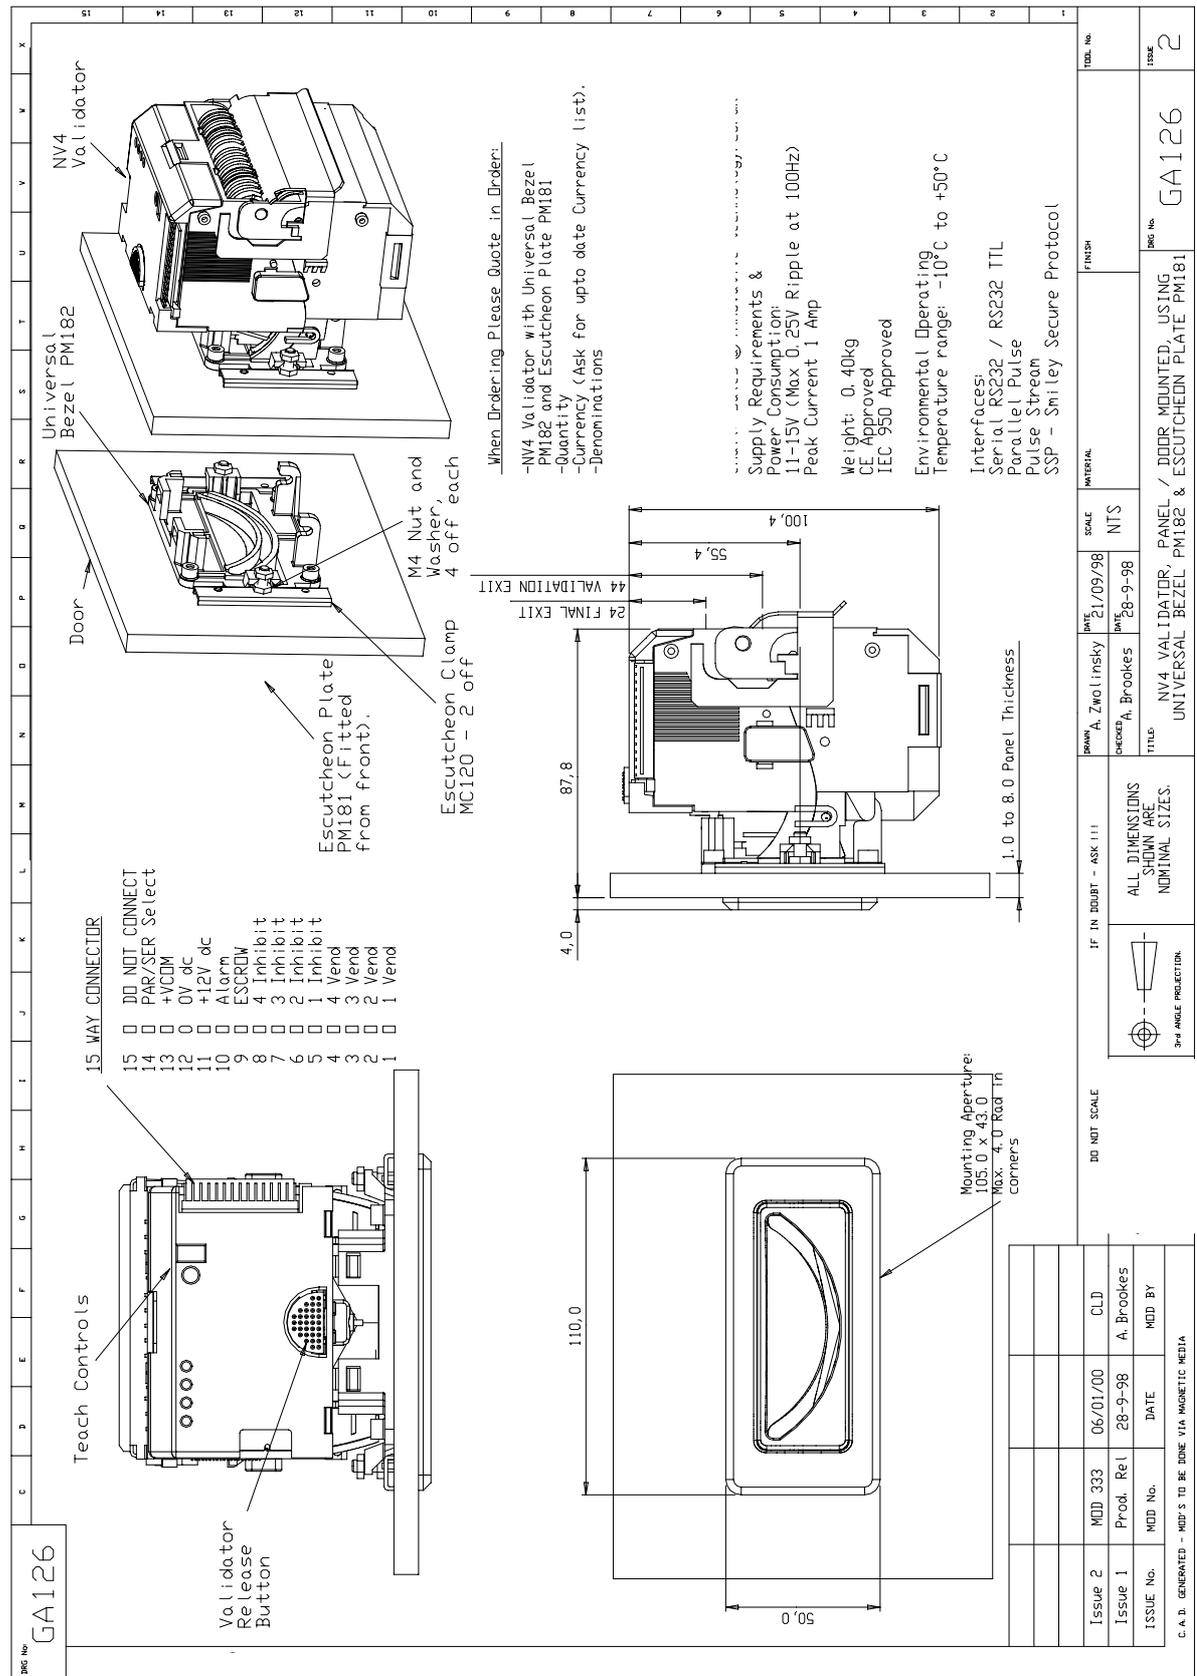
NV4 Befestigung an Fronttuer mit Universal Frontblende und Escutcheon Plate
